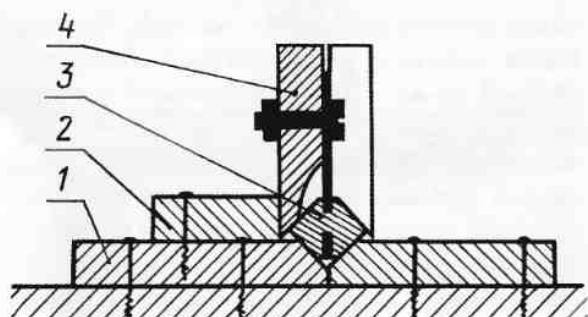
Поперечный разрез ложа для прорезания пазов на горбылке: 1 — направляющие планки со скосом кромок под углом 45°; 2 — опорная рейка; 3 — заготовка горбылька; 4 — пазанок
